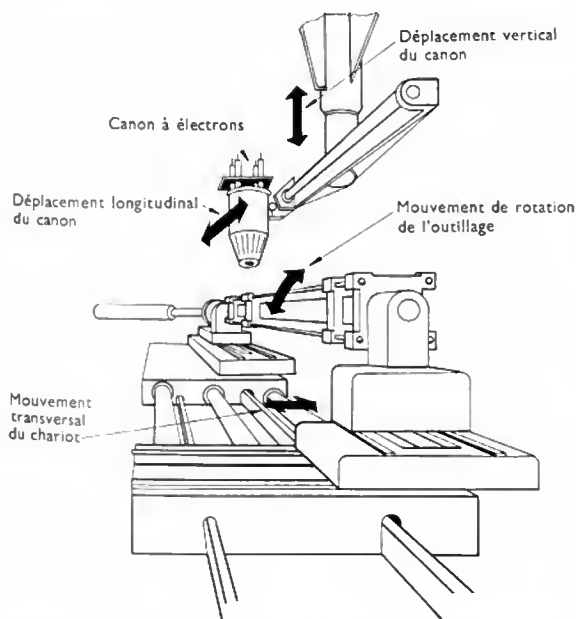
Intérieur d'une machine à souder par faisceaux d'électrons pour assemblage d'éléments de grandes dimensions
